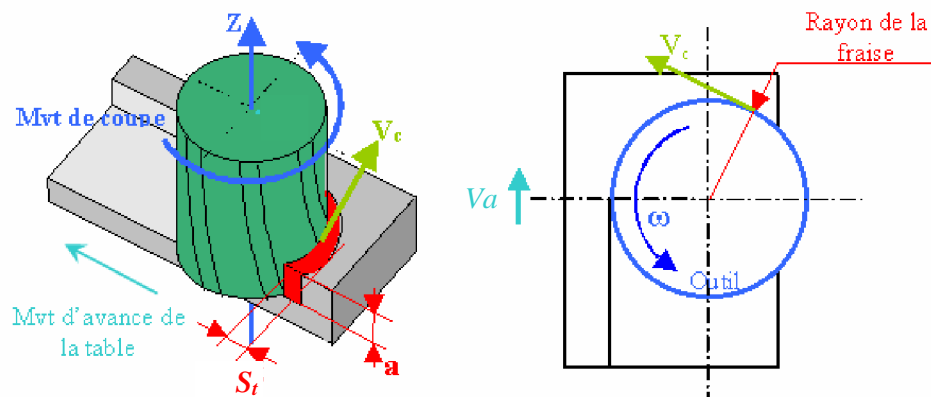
Mouvements de la fraise par rapport à la pièce.
